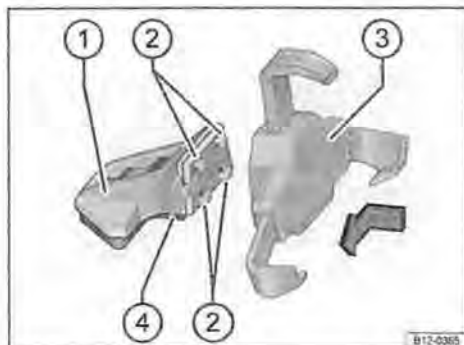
Assemblaggio del supporto universale e del bracciolo
